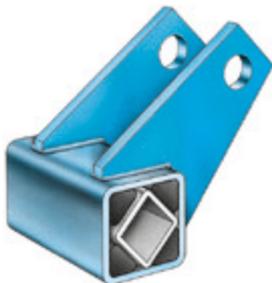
Aussenrohr mit aufgeschweissten Hebelarmen
